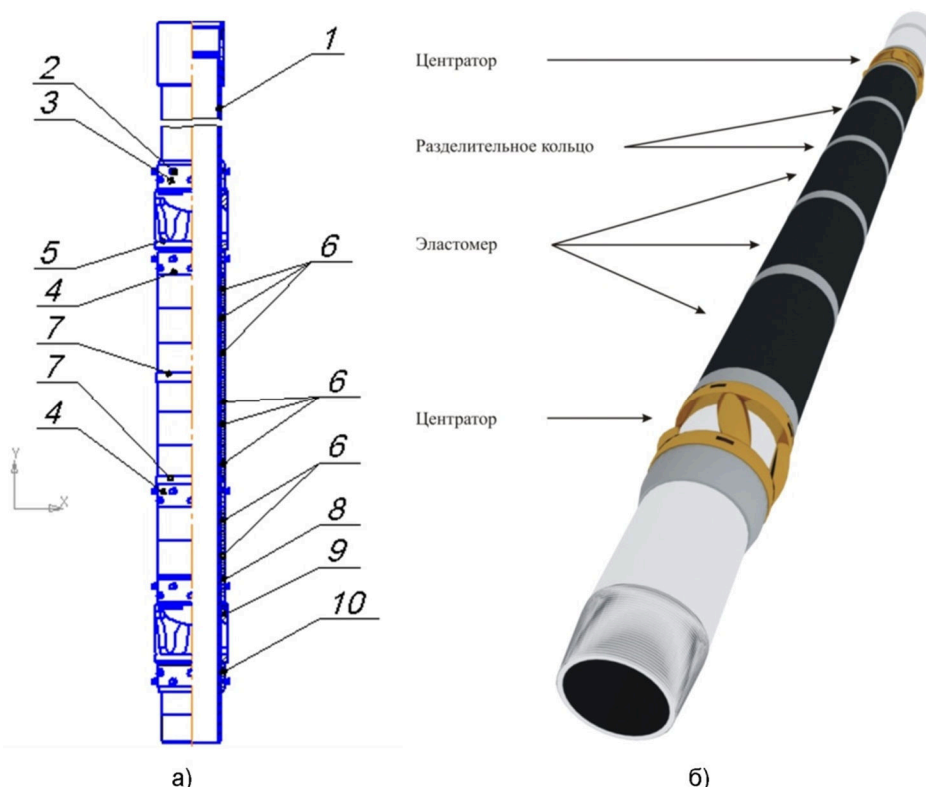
Набухающий пакер: а) сборочный вид; б) вид в аксонометрии
